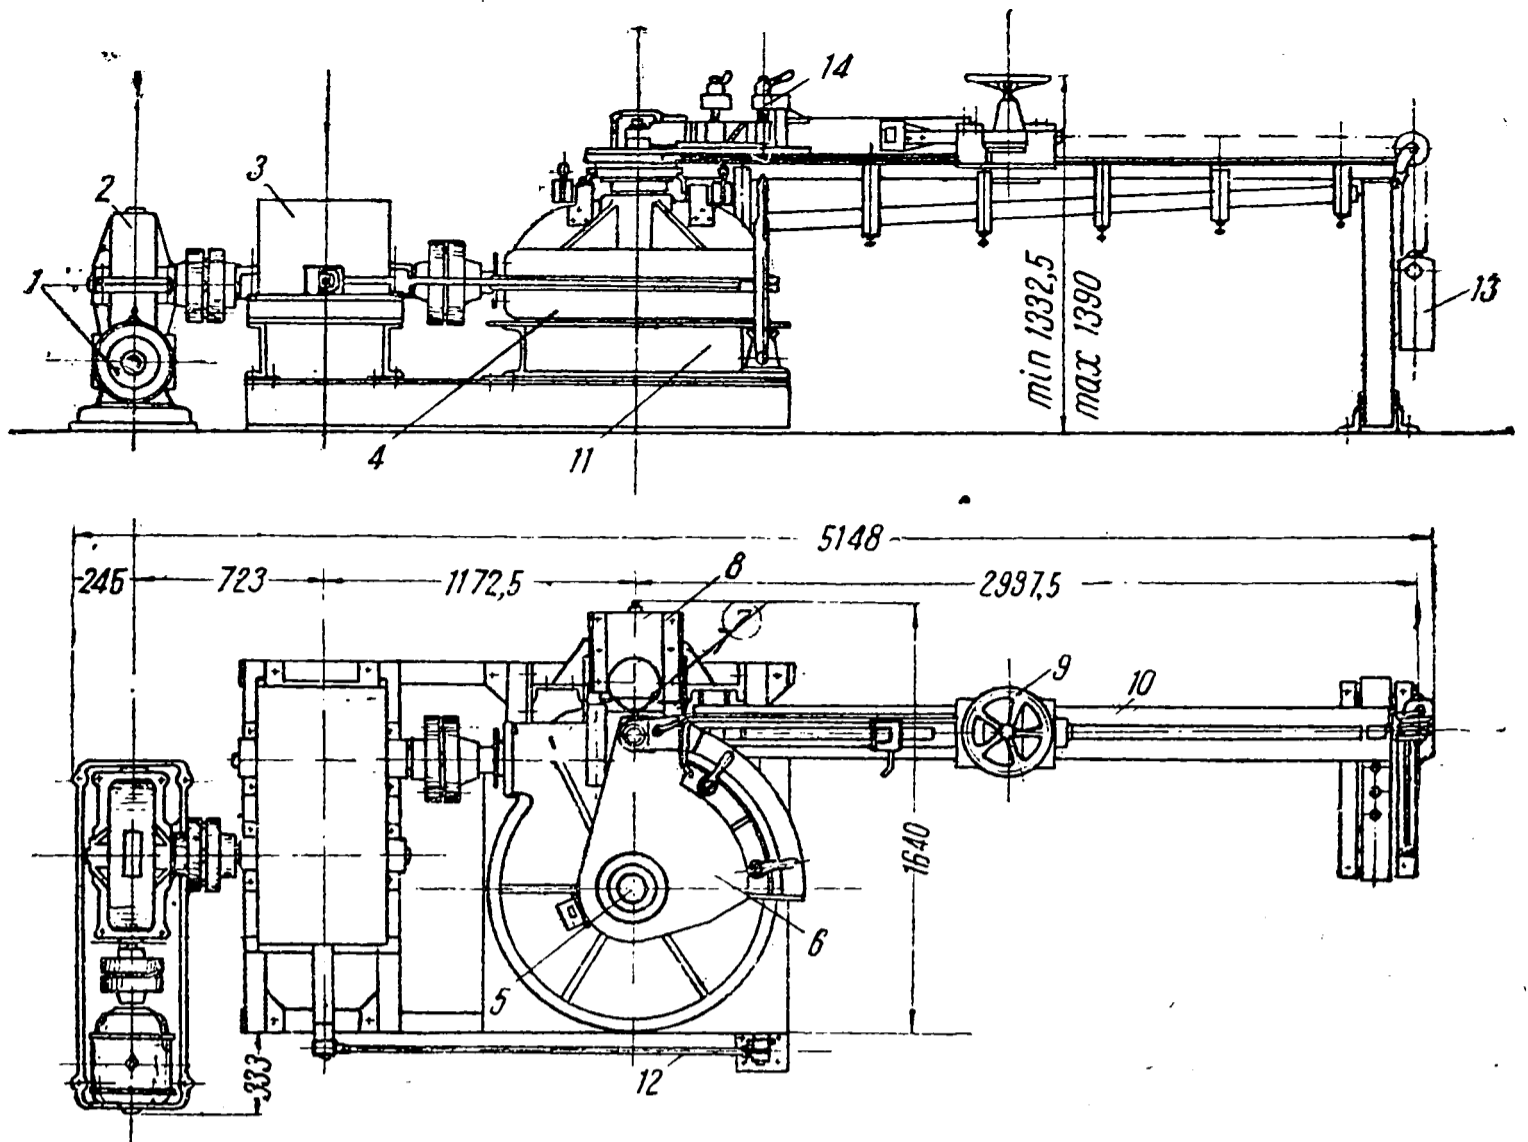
Гнутарный станок промышленного типа для косяков и полуободьев:
